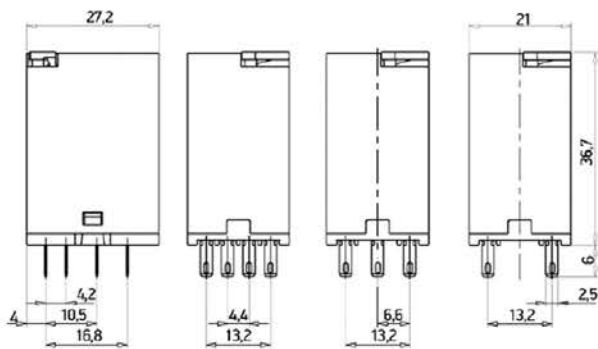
Габаритные, установочные, присоединительные размеры реле OptiRel G RP55-3X с кнопкой «Тест»
